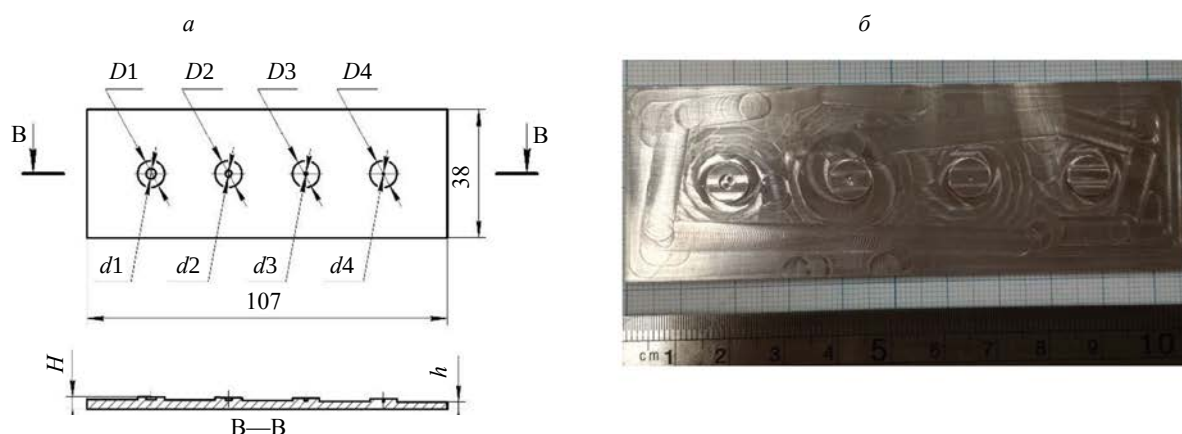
Образец настроечный с имитаторами дефектов типа непровар и имитаторами сварных зон: эскиз (а); общий вид (б).
